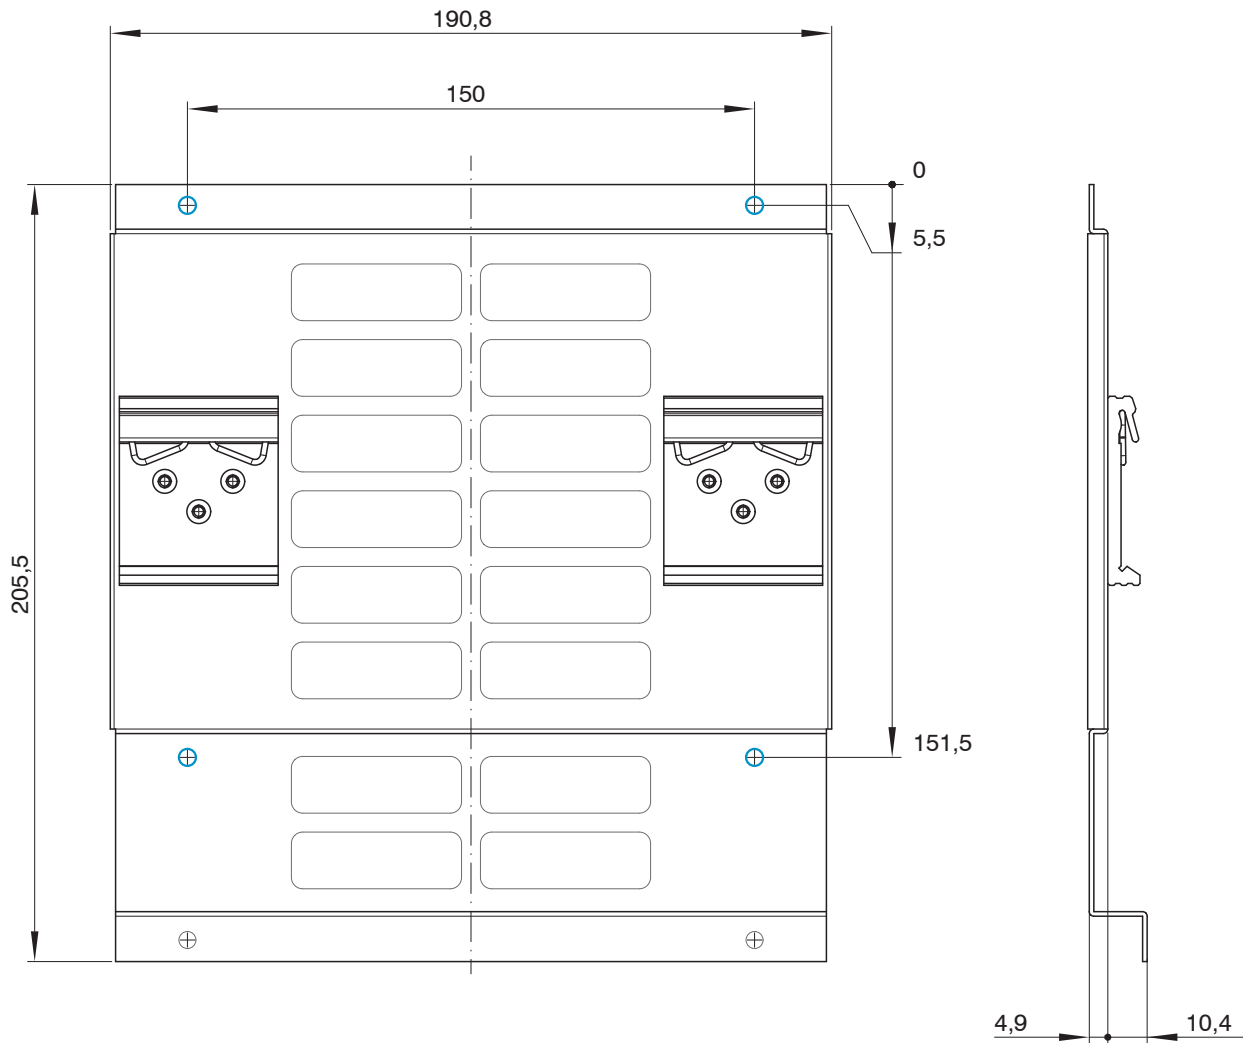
Maßzeichnung Montageplatte für Hutschiennenmontage
